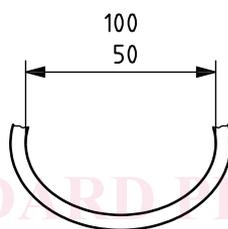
Размеры стандартного судового приспособления для пристегивания
